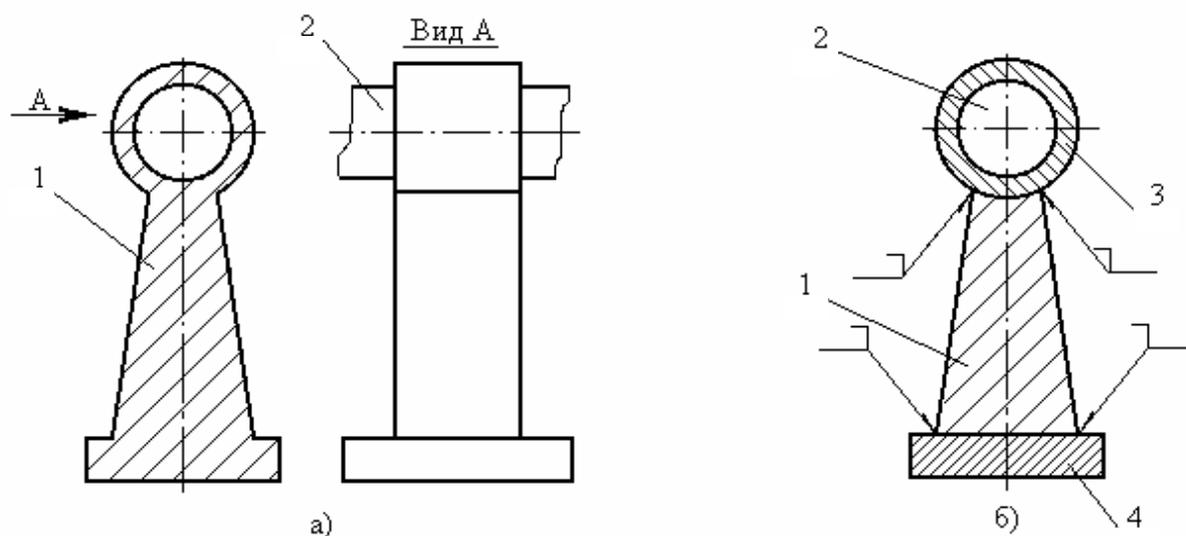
Нанесение штриховки на чертежах сварных изделий
